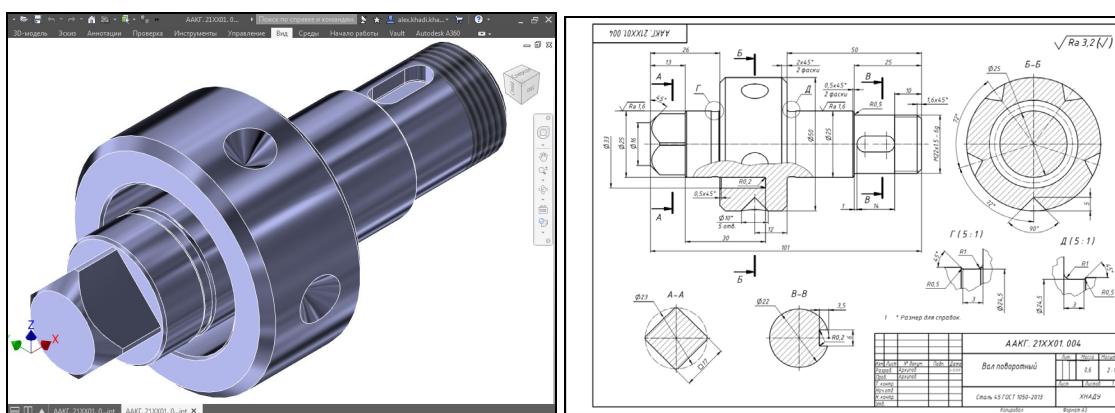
Модель та робочий кресленик деталі "Вал поворотний".
